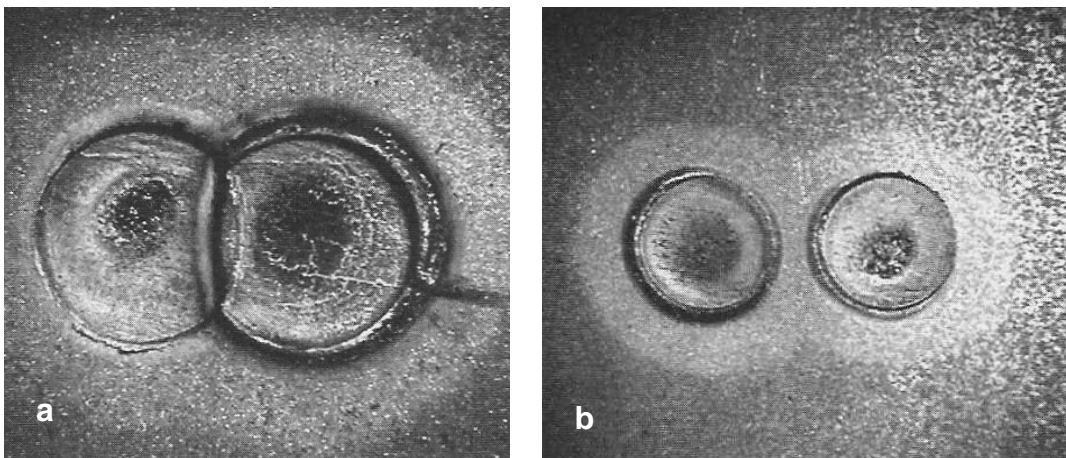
16. Discontinuidades debido a la soldadura fuera de lugar.<sup>24</sup>
